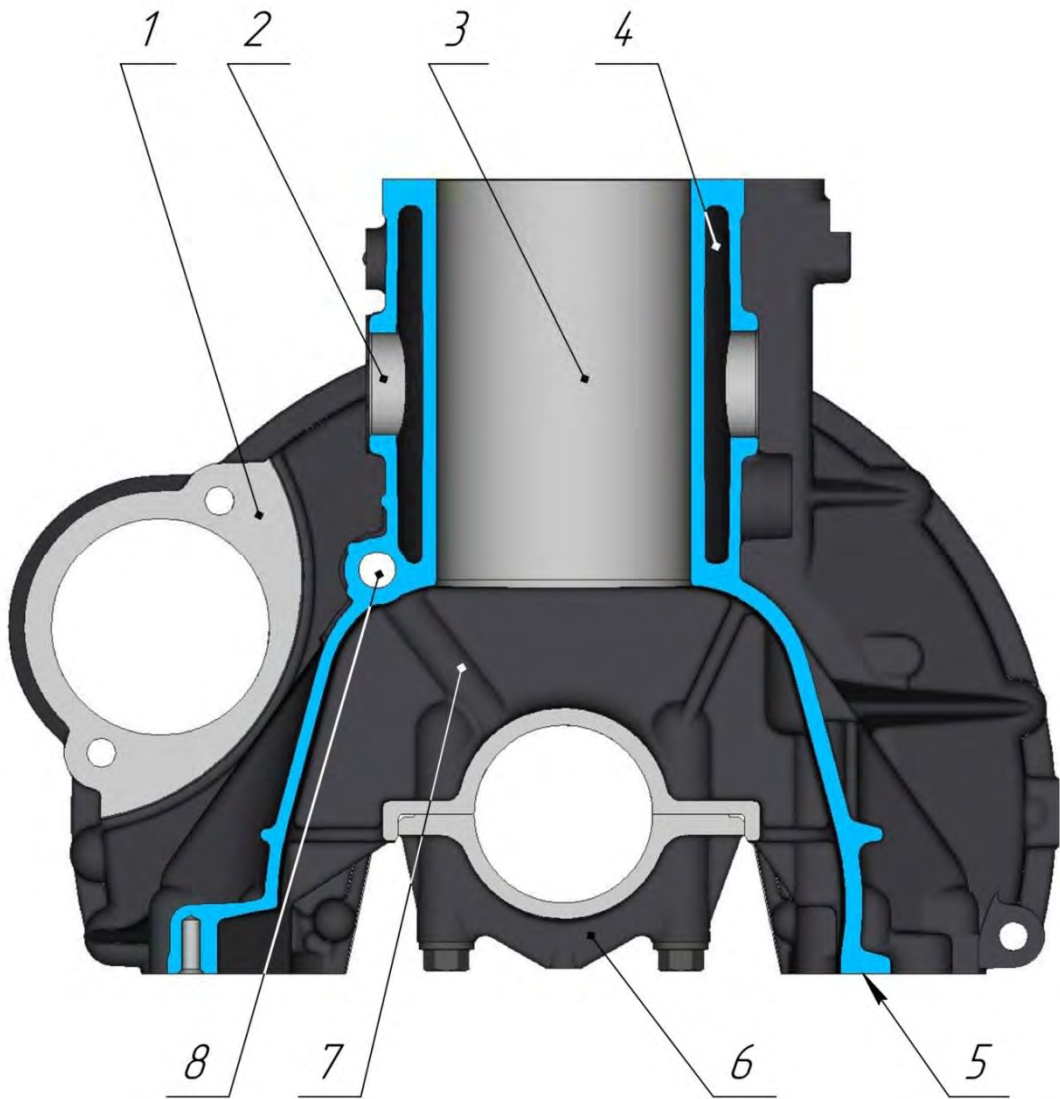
Zylinderblock. Querschnitt entlang der Zylinderachse:
